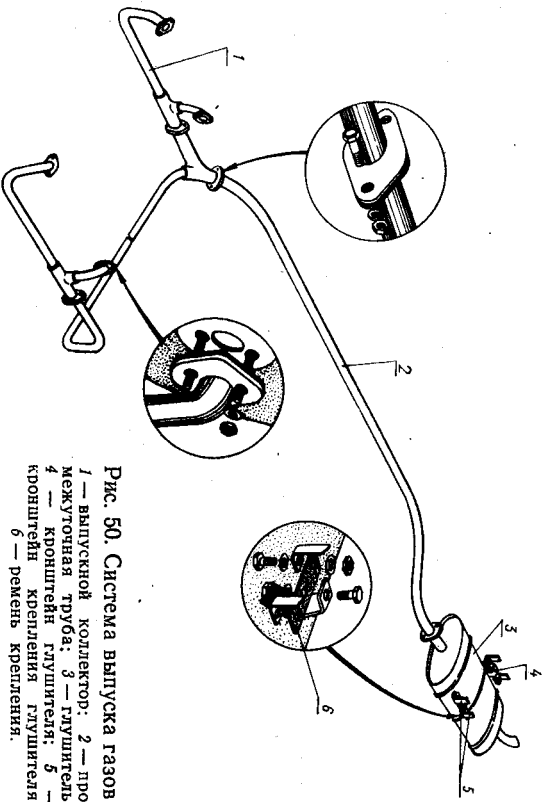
Система выпуска газов: 1 — выпускной коллектор; 2 — промежуточная труба; 3 — глушитель; 4 — кронштейн глушителя; 5 — кронштейн крепления глушителя; 6 — ремешок крепления.
